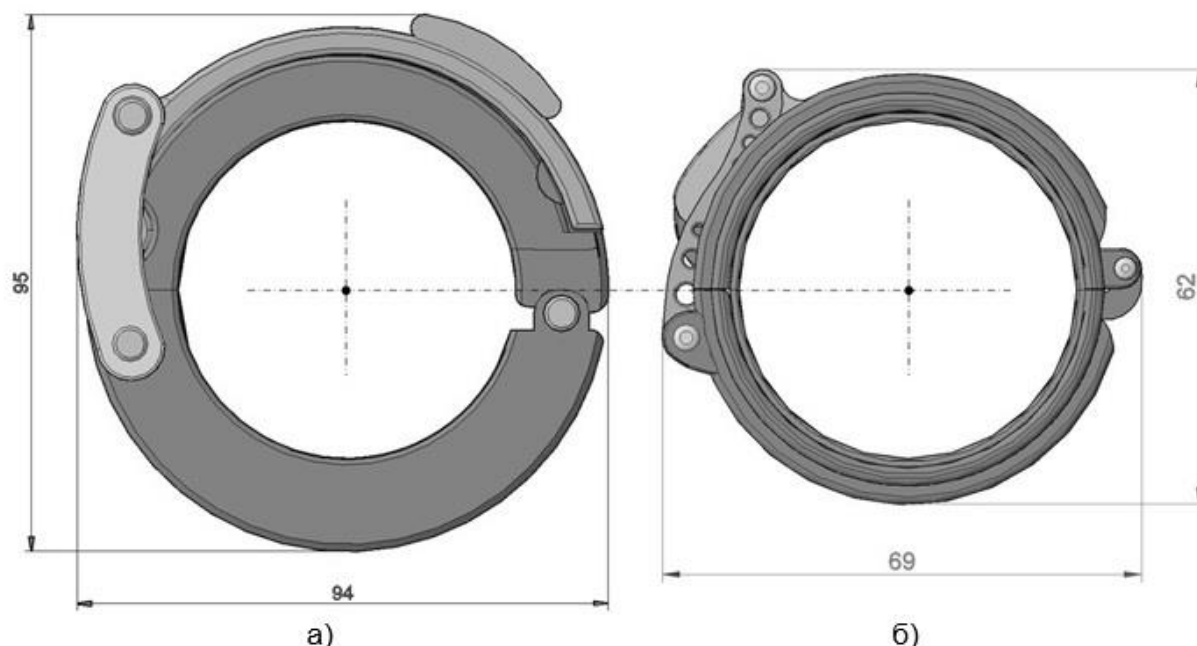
Зажим в закрытом положении (главный вид): а – старого образца; б – нового образца
